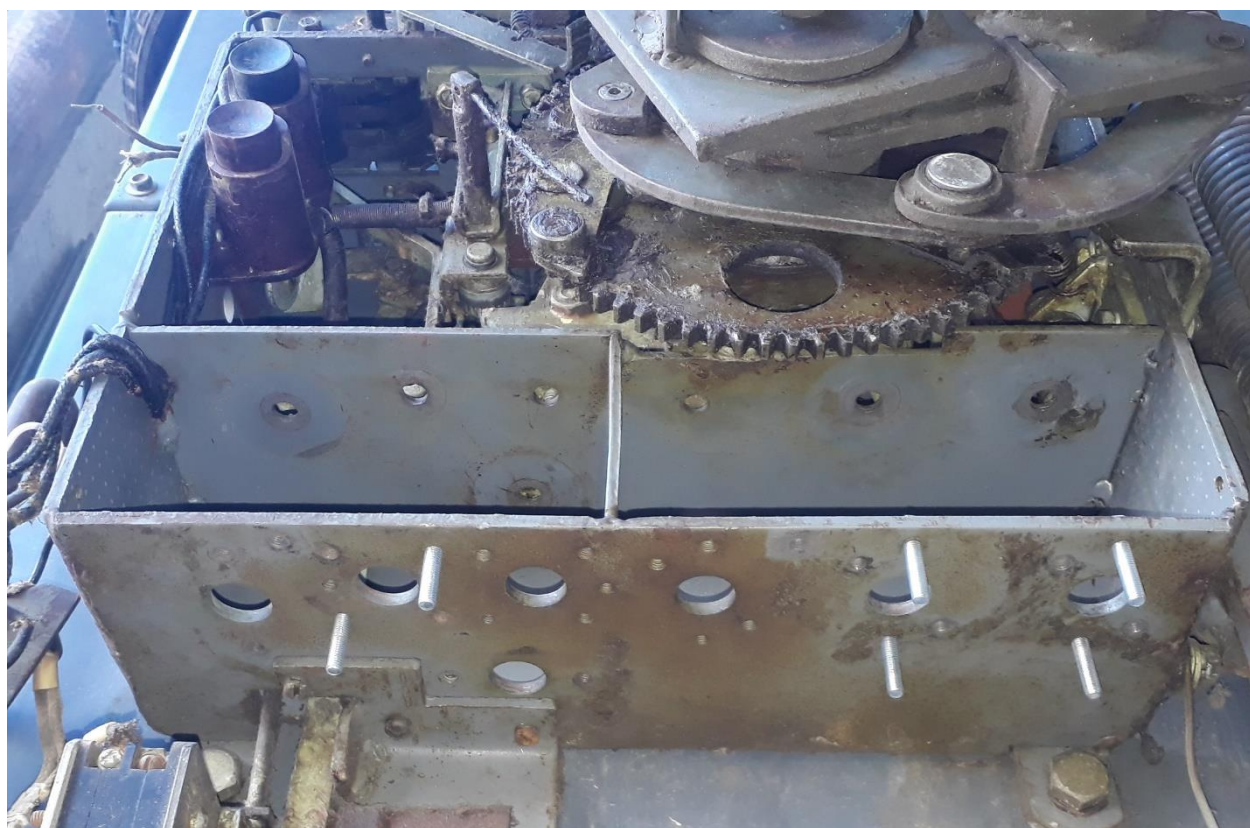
б. Установка винтов М6х30. Вид снизу.
